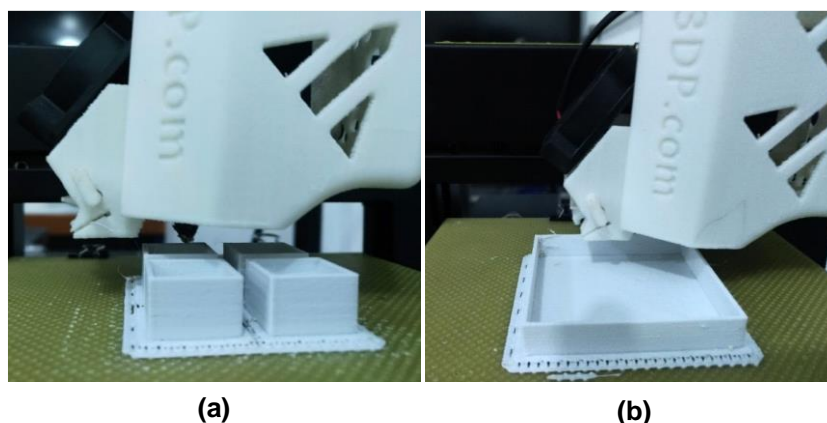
Divisão do processo de impressão: (a) Impressão dos cubos; (b) Impressão das caixas.
